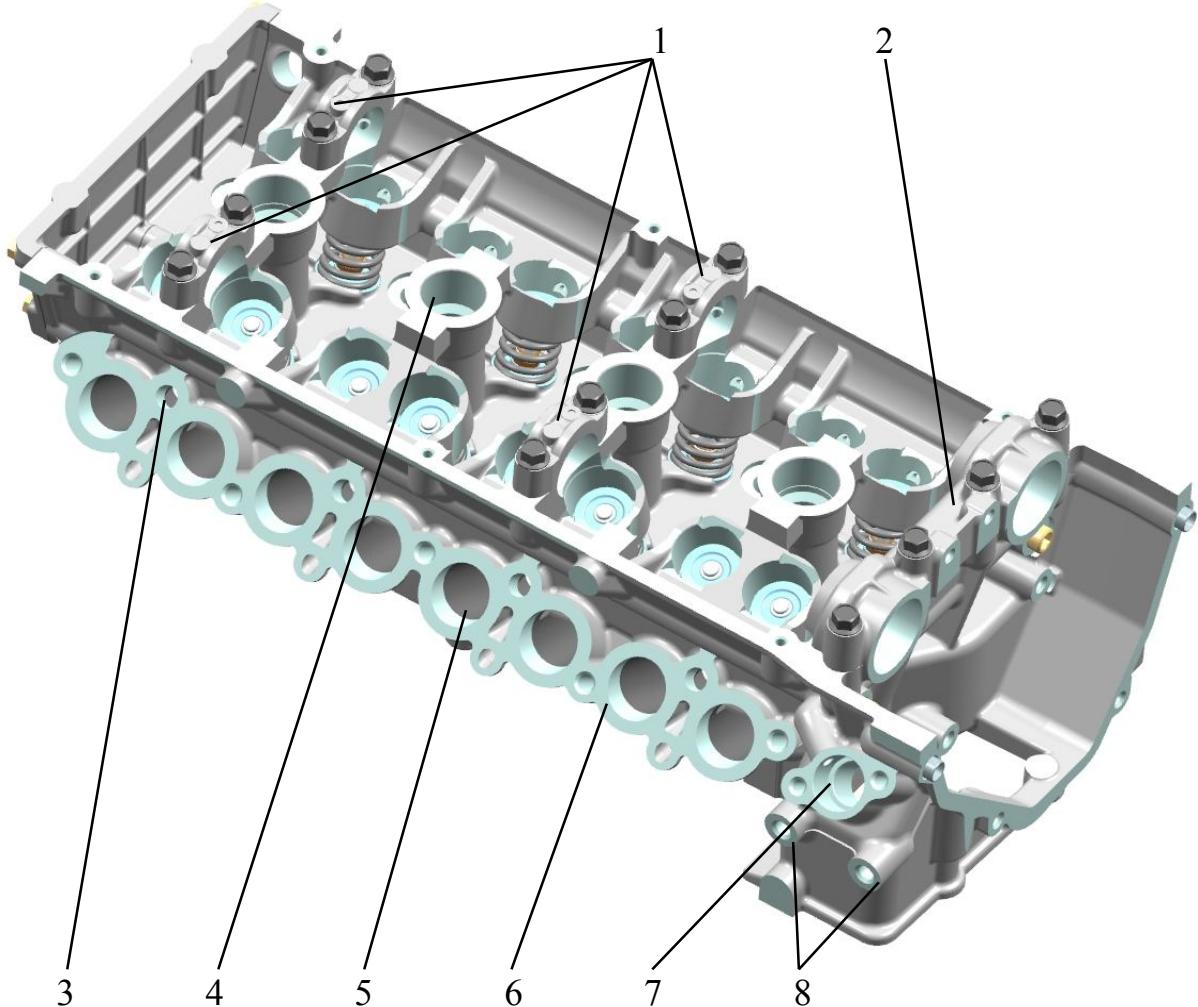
Головка цилиндров. Вид на фланец впускной трубы, на верхнюю плоскость и на фланец передней крышки:
